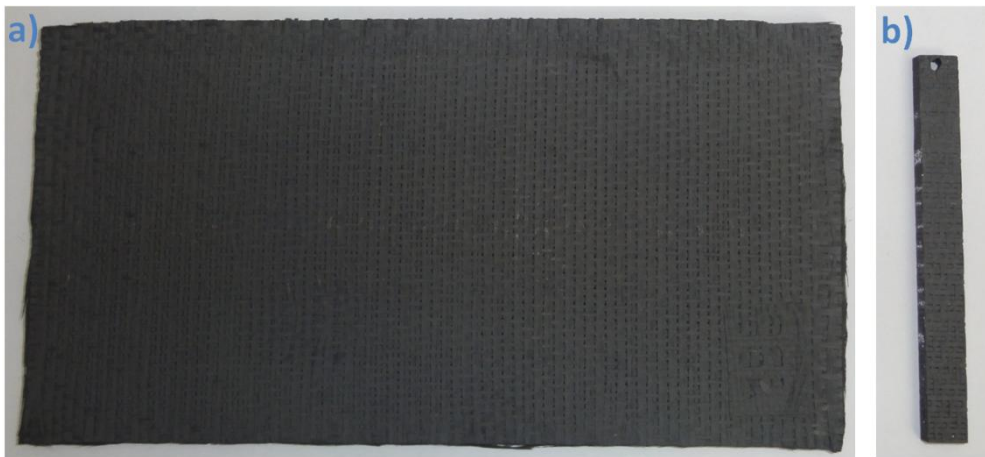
Photographies de préformes en SiC stade CVI : a) une plaque de dimensions $200 \times 110 \times 3 \text{ mm}$ et b) une languette de dimensions $100 \times 10 \times 3 \text{ mm}$ issue de l'usinage de la plaque
